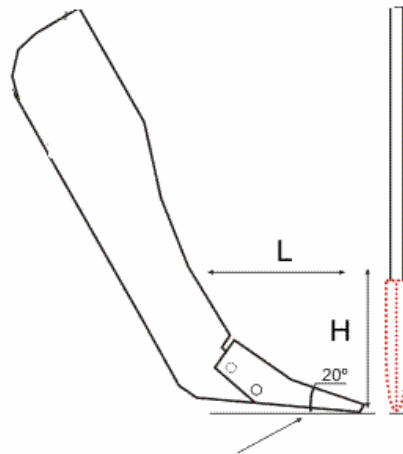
Haste e ponteira sulcadora removível utilizada no ensaio.
